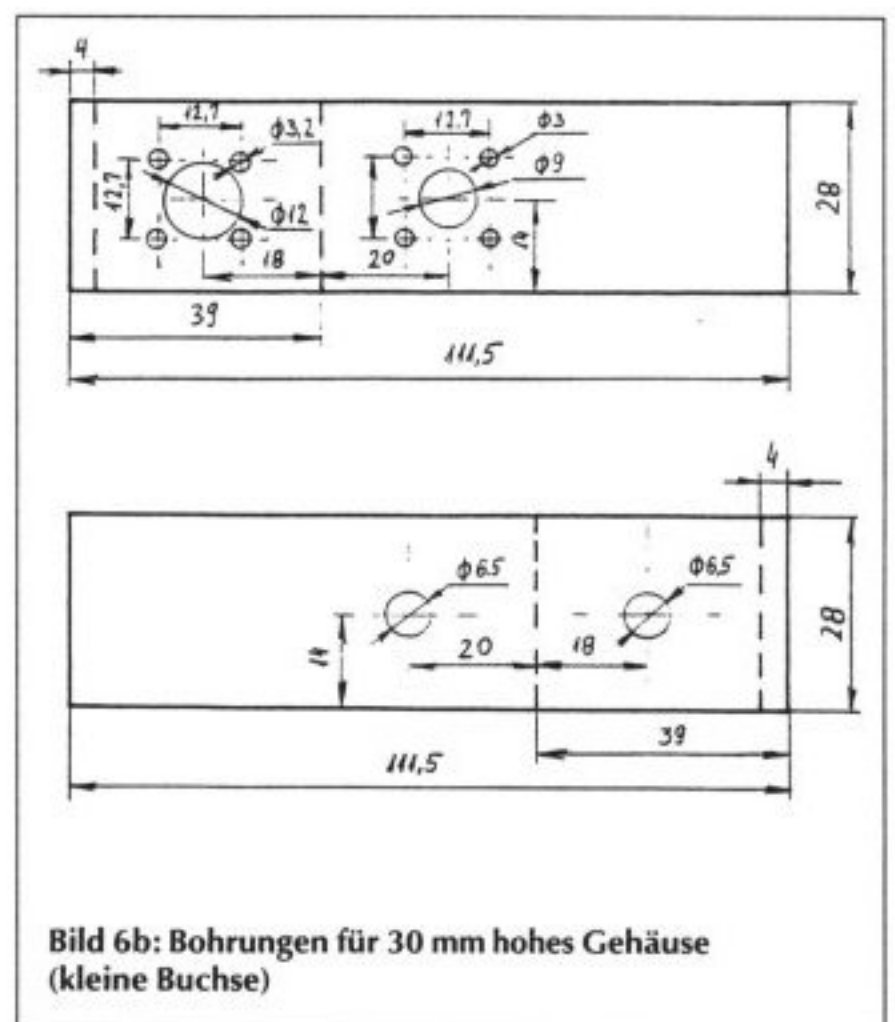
Bohrungen für 30 mm hohes Gehäuse (kleine Buchse)
